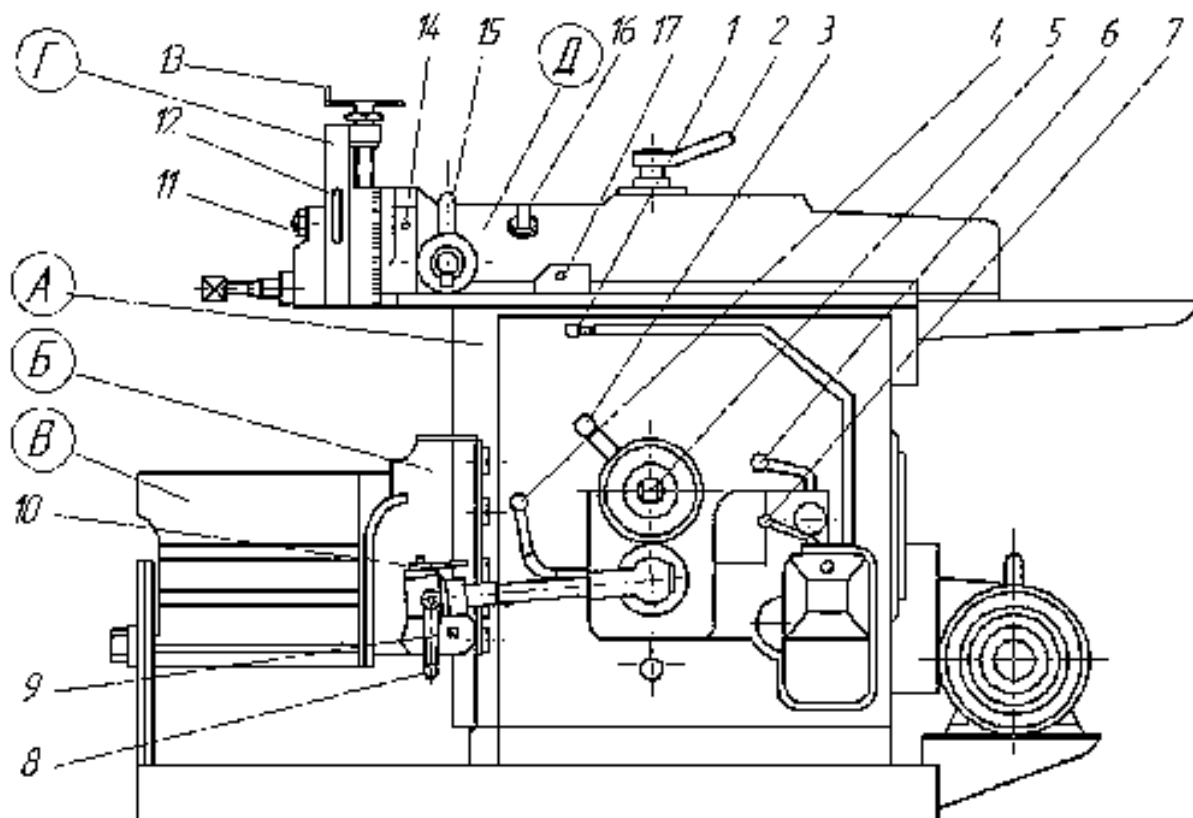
Общий вид и рукоятки управления поперечно-строгального станка 7Б35: А – станина; Б – салазки крестовые; В – стол; Г – суппорт поворотный; Д – ползун; 1 – рукоятка включения фрикциона; 2 – рукоятка зажима ползуна; 3 – рукоятка переключения поперечных подач стола; 4 – рукоятка ускоренного перемещения; 5 – квадрат для установки длины хода ползуна; 6 – рукоятка переключения перебора; 7 – рукоятка переключения скоростей (частот двойных ходов) ползуна; 8 – рукоятка ручного перемещения стола; 9 – квадрат для установки вертикального перемещения стола; 10 – рукоятка реверса подачи; 11 – гайка зажима поворотной доски; 12 – рукоятка зажима салазок суппорта; 13 – рукоятка вертикального перемещения суппорта; 14 – рукоятка зажима суппорта; 15 – рукоятка переключения вертикальных подач суппорта; 16 – квадрат установки места хода ползуна; 17 – кулачок автоматической подачи суппорта
